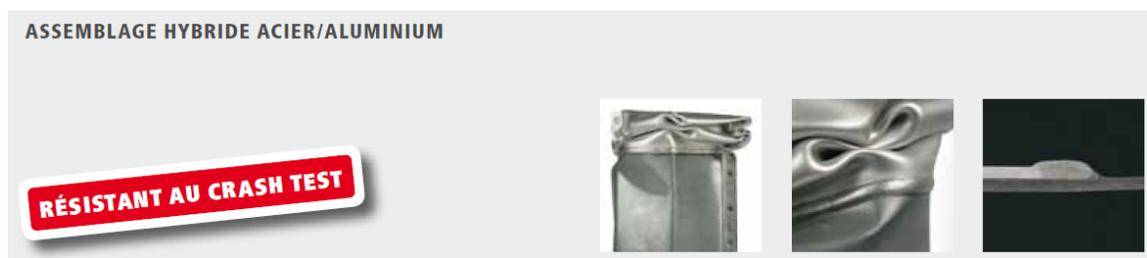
Soudure CMT aluminium sur acier galvanisé, test de collision⁷
